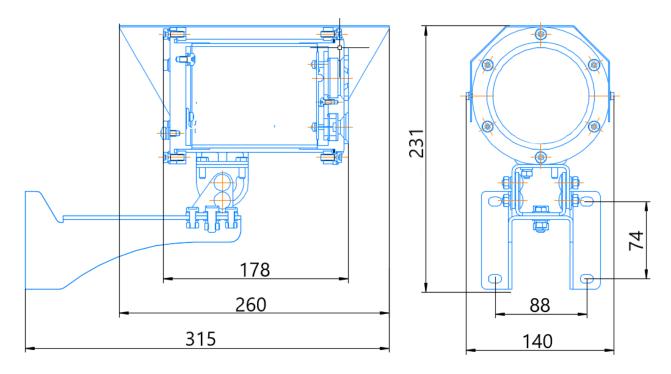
Габаритные размеры извещателя с крепежно-юстировочным устройством
